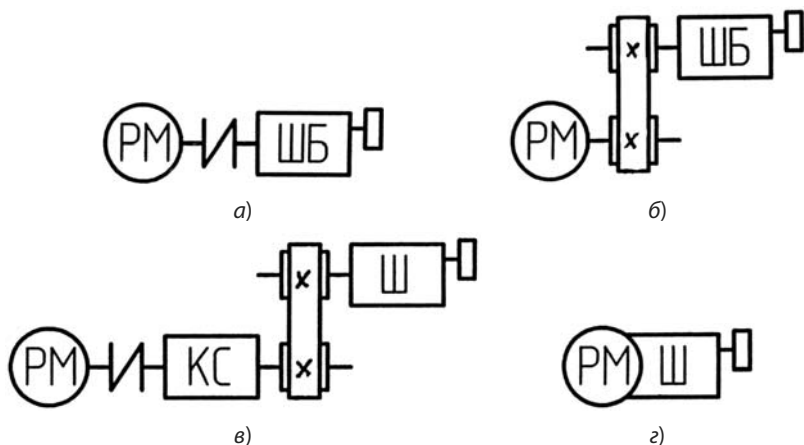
Схемы построения приводов главного движения в станках с ЧПУ
